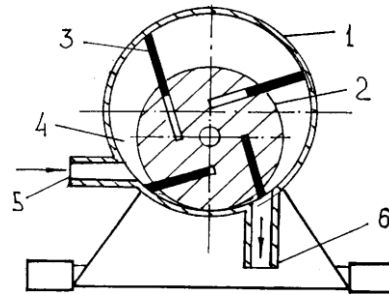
Схема пластинчатого вакуумного насоса з ексцентричним розташуванням ротора: 1 – корпус; 2 – ротор; 3 – пластина; 4 – камера всмоктування; 5 – всмоктувальний патрубок; 6 – вихлопна труба.
